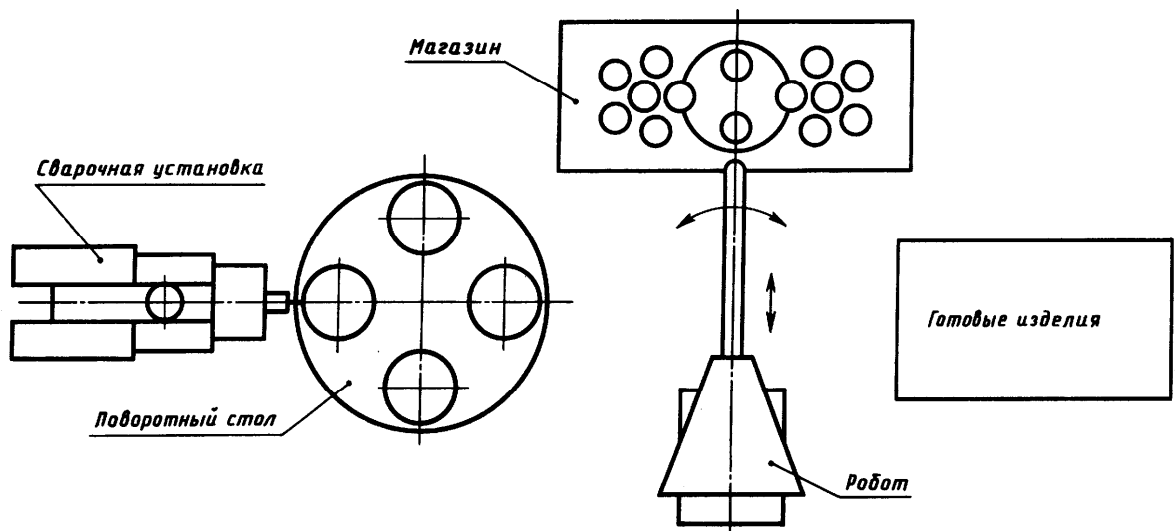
Схема РТК для сборки и сварки кулачковой муфты
